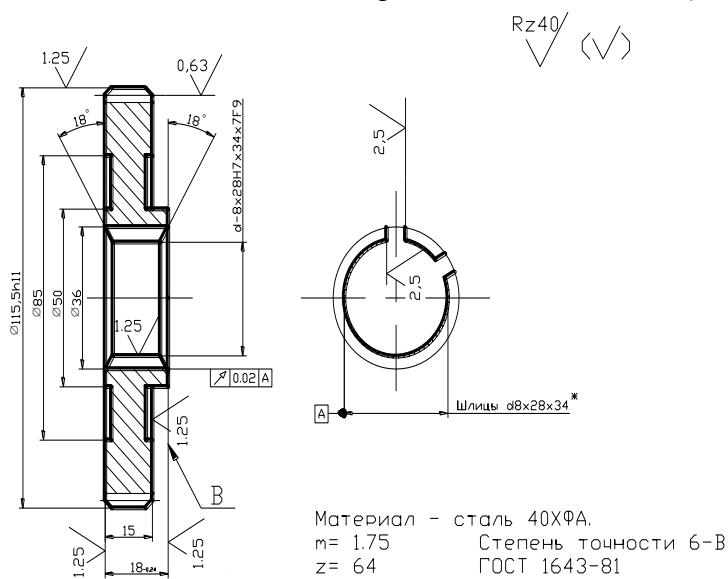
Зубчатое колесо сменное. (Сталь 40ХФА).
